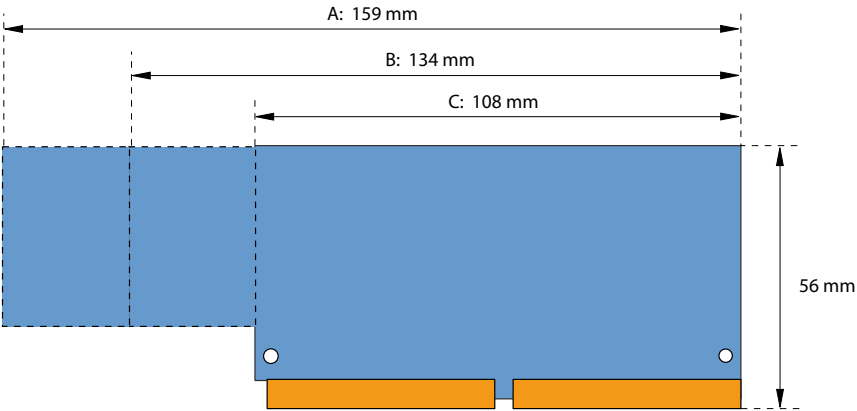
Dimensions des cartes d'interface (formes de construction A, B , C)
